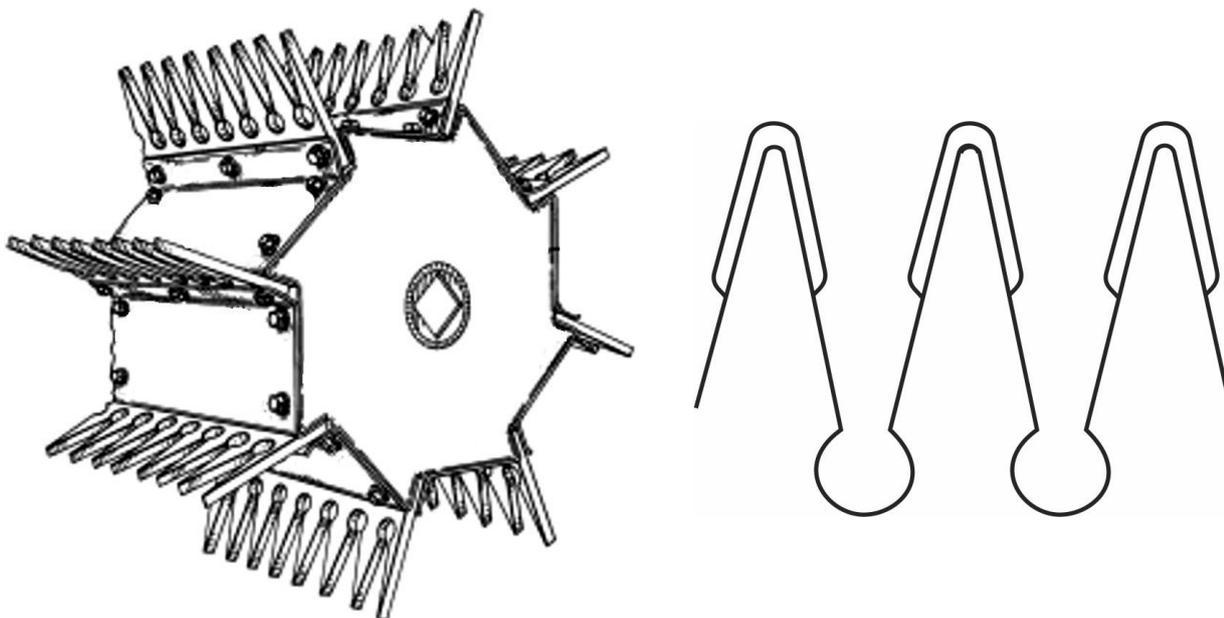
A la izquierda un corte del tambor desgranador del cabezal stripper (Klinner 1988), y a la derecha un corte de un peine desgranador como los que se montan en el tambor (Shelbourne, 2001).
